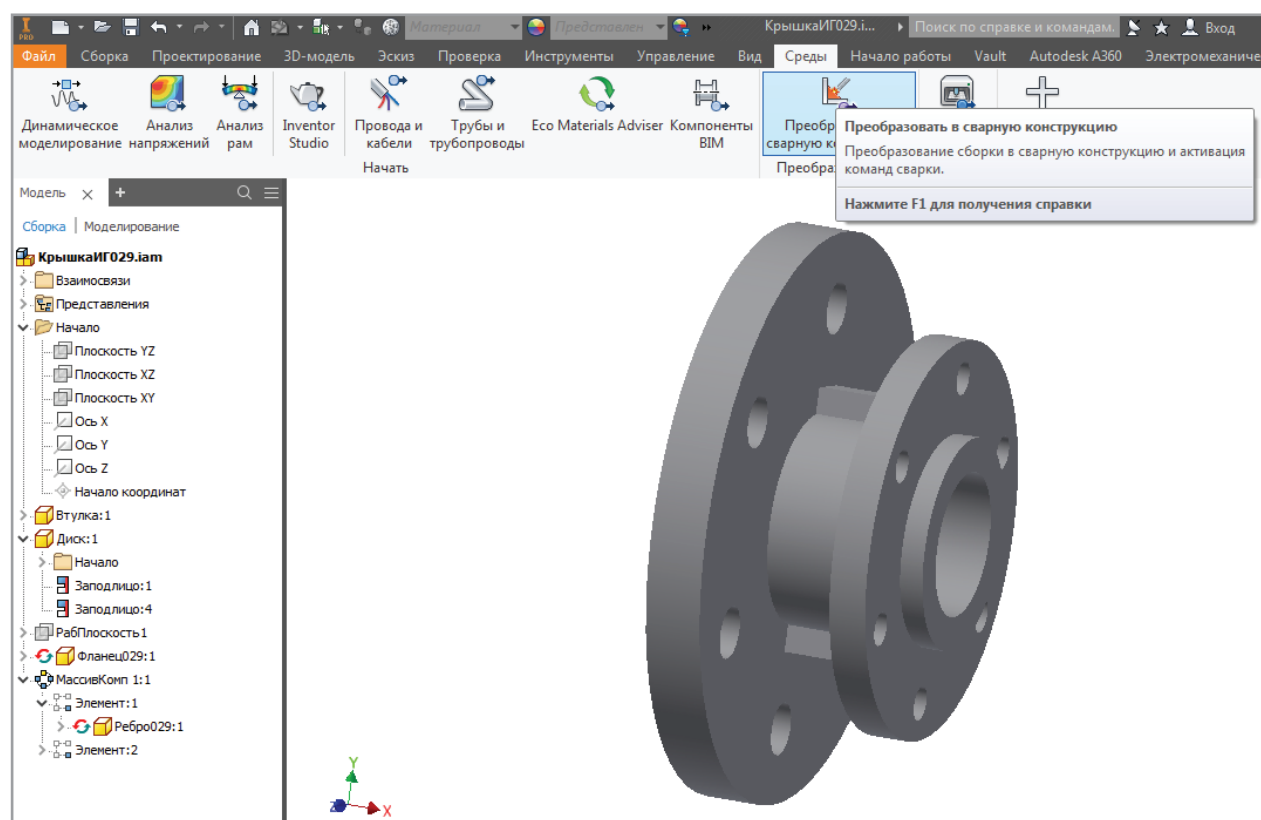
Преобразование модели в сварную конструкцию
